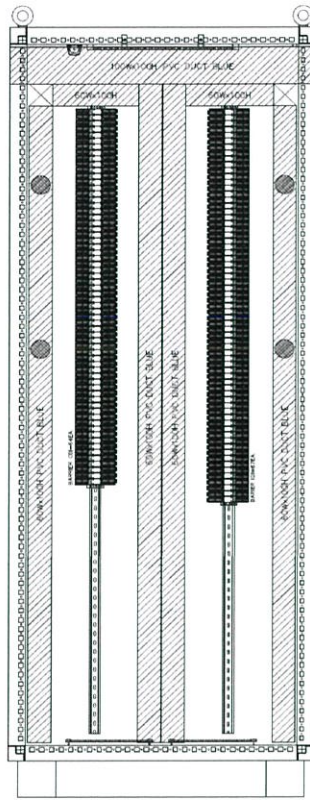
Layout ด้านหน้าตู้ Marshalling 1
